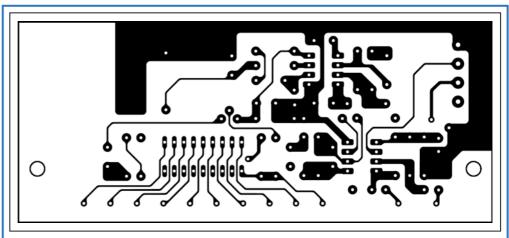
Dessin, à l'échelle 1, de la face soudures la platine voltmètre/buzzer.
